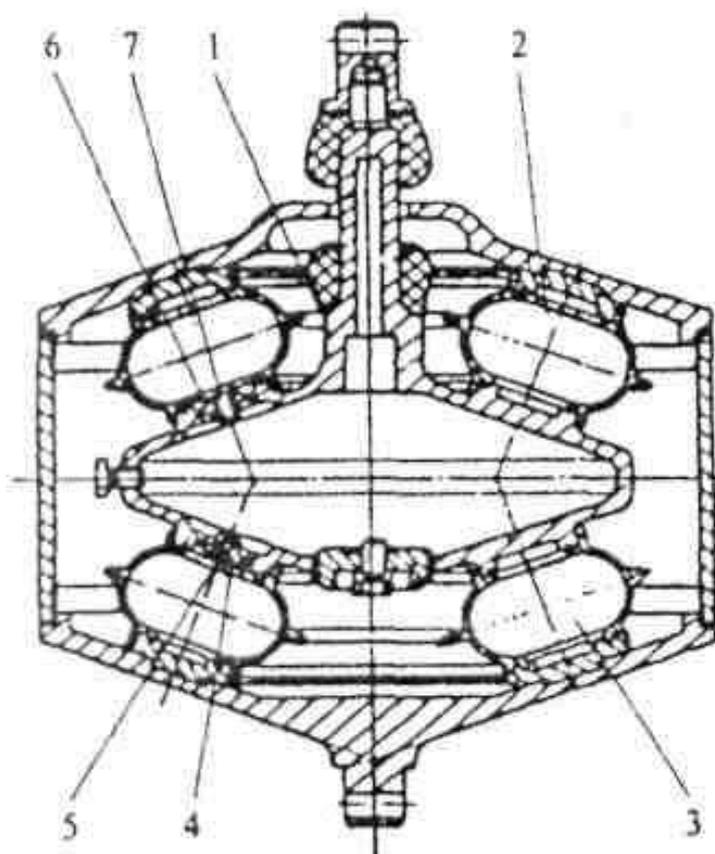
Виброизолятор с резиновыми элементами
